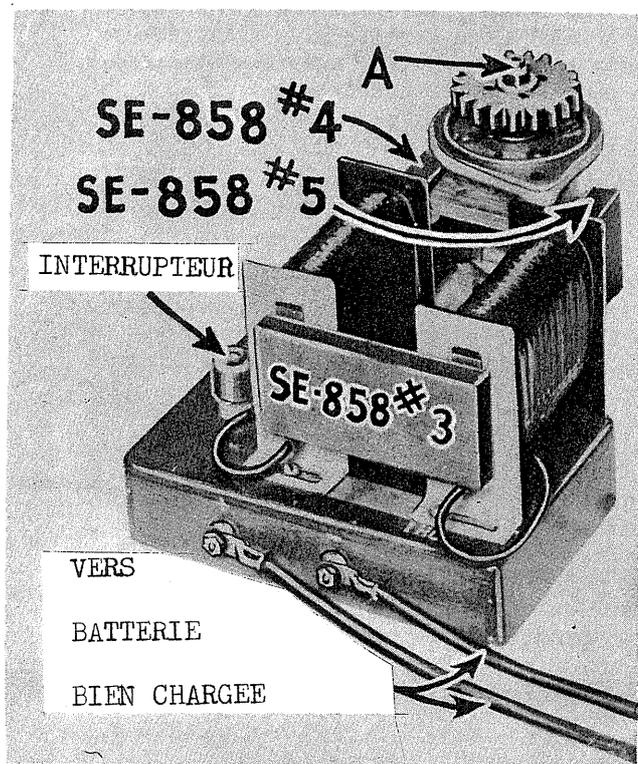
MAGNETO WICO TYPE "AH" EN POSITION POUR ETRE RECHARGÉE PAR LE MAGNETISEUR A BOBINES SE-858.
